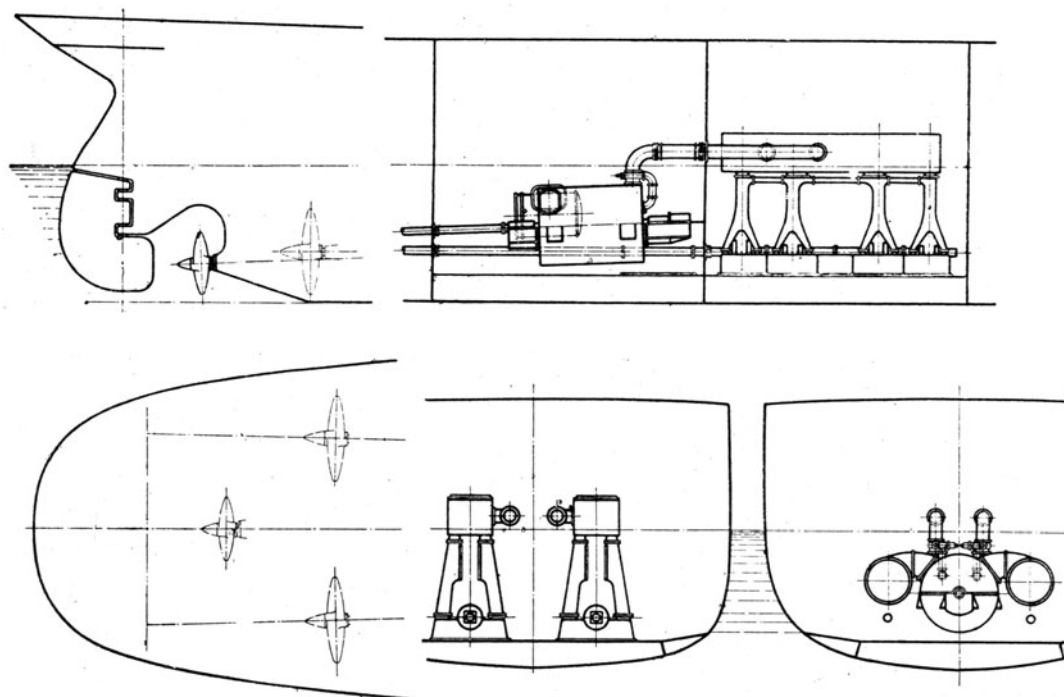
Hochdruckkolbenmaschinen mit Niederdruckturbine.
